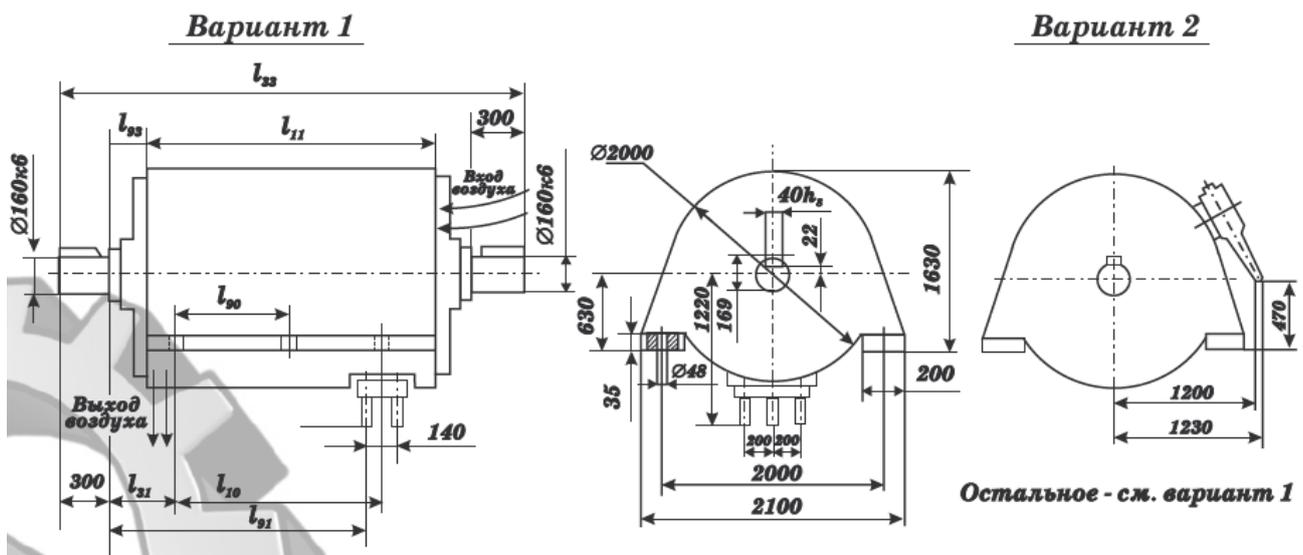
Габаритные, установочные размеры двигателей СДЭ2 17-го габарита с частотой вращения 1000 об/мин
